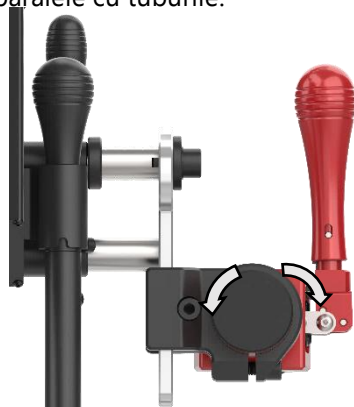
Schimbarea unghiului frontal al fălcilor de prindere.
